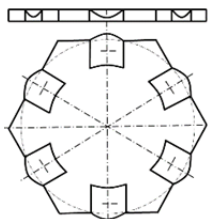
Исходная заготовка с утонением толщины материала в виде цилиндрических желобов [11]
